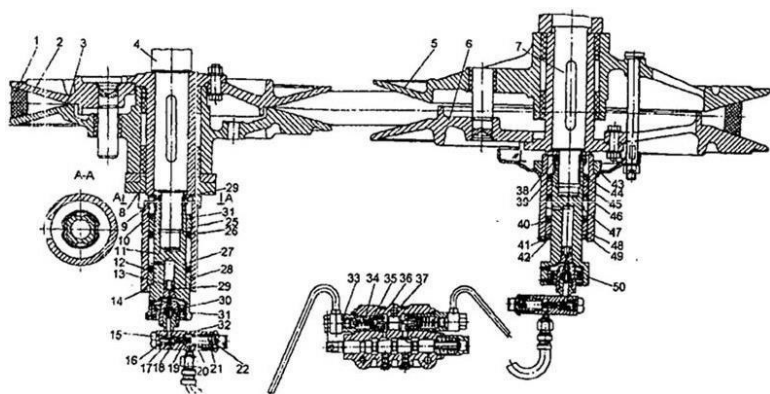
Гидрофицированный вариатор барабана:
